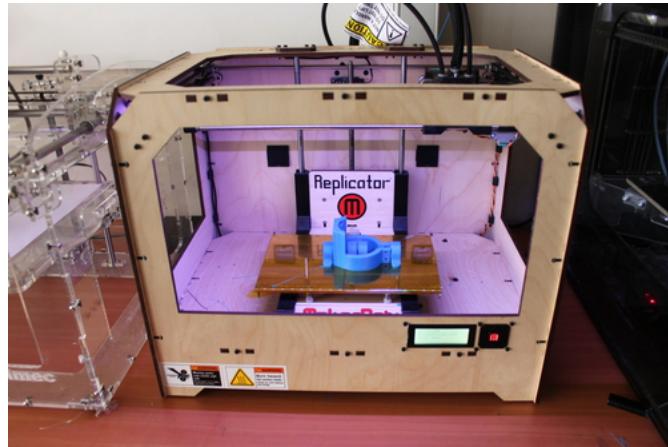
Replicator 1 de Makerbot, impresora 3D FDM utilizada para prototipar chasis y ruedas de robot MODI. En Laboratorio de Síntesis de maquinas inteligentes de la Universidad de Chile, junto a la Fab@Home y 3DTouch.
